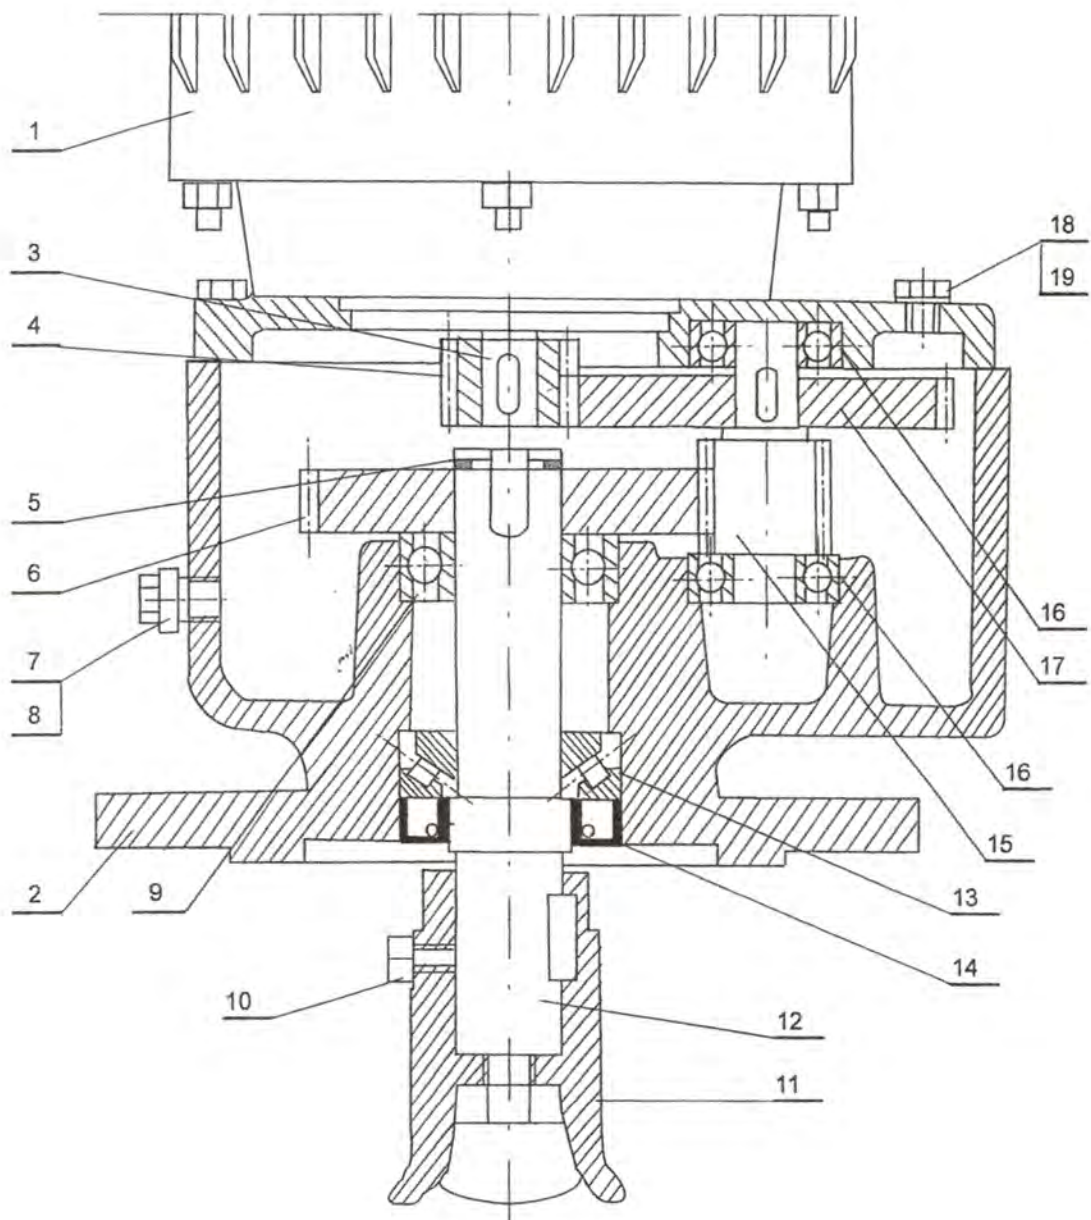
МОТОРЕДУКТОР МЕШАЛКИ И ВИНТОВОГО НАСОСА
